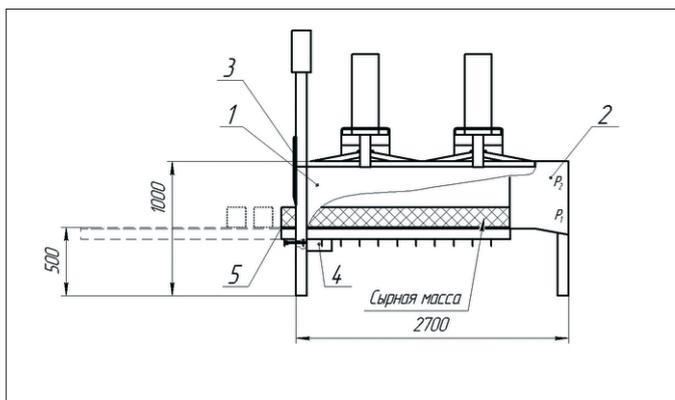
Схема формовочного аппарата АФ-300/А: 1 – ванна; 2 – бункер для сбора сыворотки; 3 – нож поперечный; 4 – выдвижной механизм; 5 – выдвижной под
